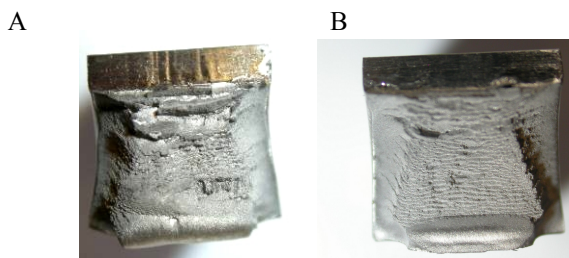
Superfície fraturada dos corpos de prova soldados, 80°C em (A) e 150°C em (B).
